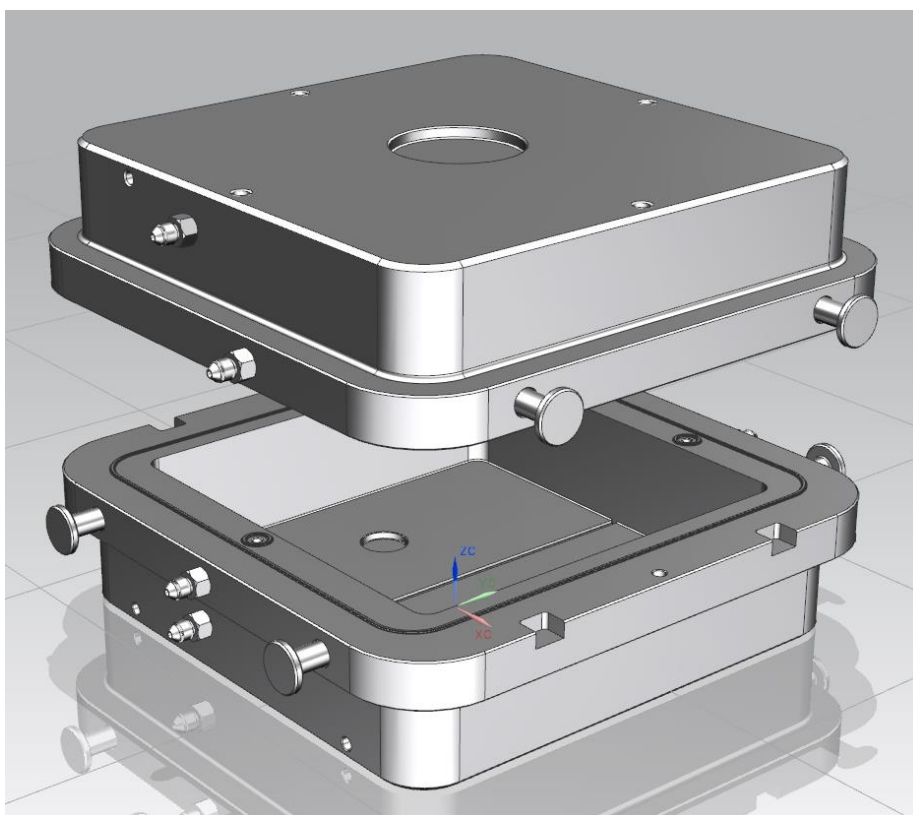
Модель блока с двумя формовочными полостями
